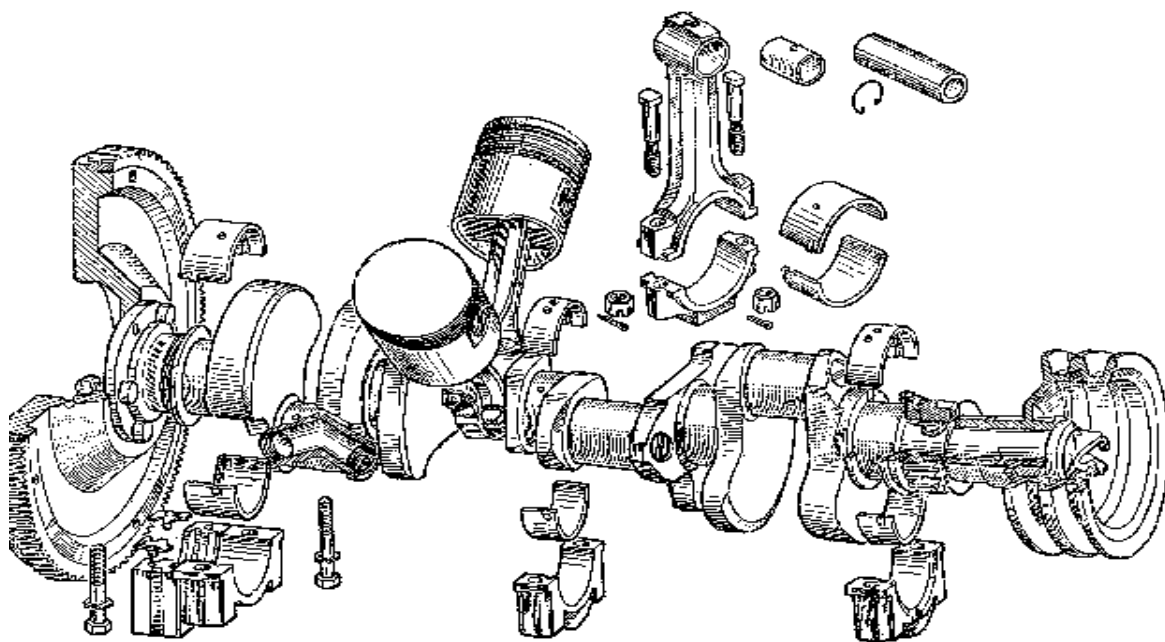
Подвижные детали КШМ V-образного двигателя
